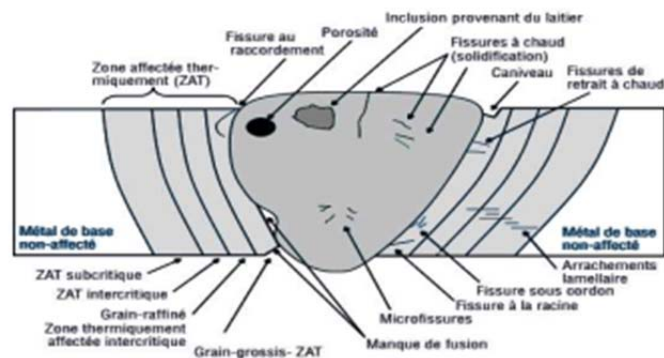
Défauts de soudage [27]. -Porosité et inclusions, - manque de fusion et pénétration, -Crevasses et fissures [26, 28, 29, 30].
